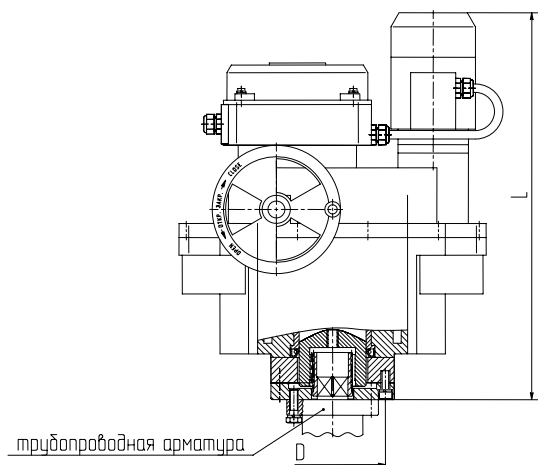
Габаритные и присоединительные размеры М30Ф-250
